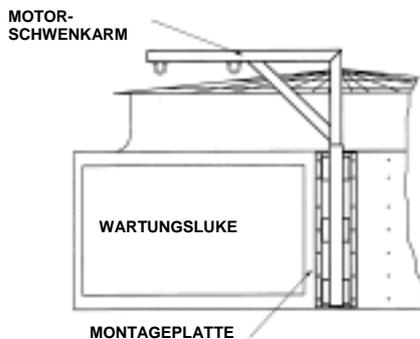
Schwenkarm mit Zwei-Punkt-Aufhängung
